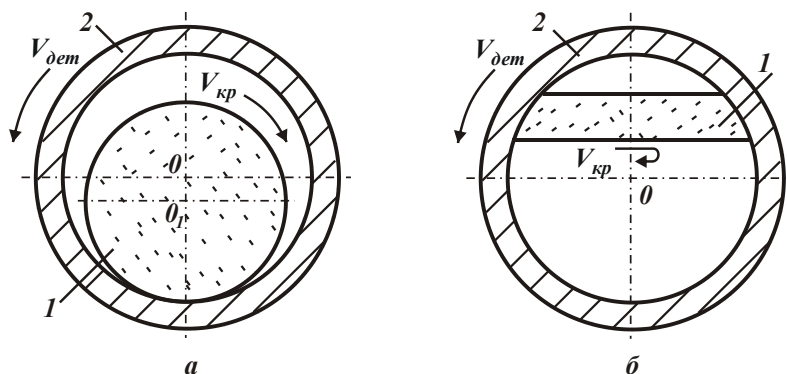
Схемы обычного внутреннего шлифования (а) и шлифования с перпендикулярным расположением осей вращения круга и детали (б): 1 – круг; 2 – обрабатываемая деталь
